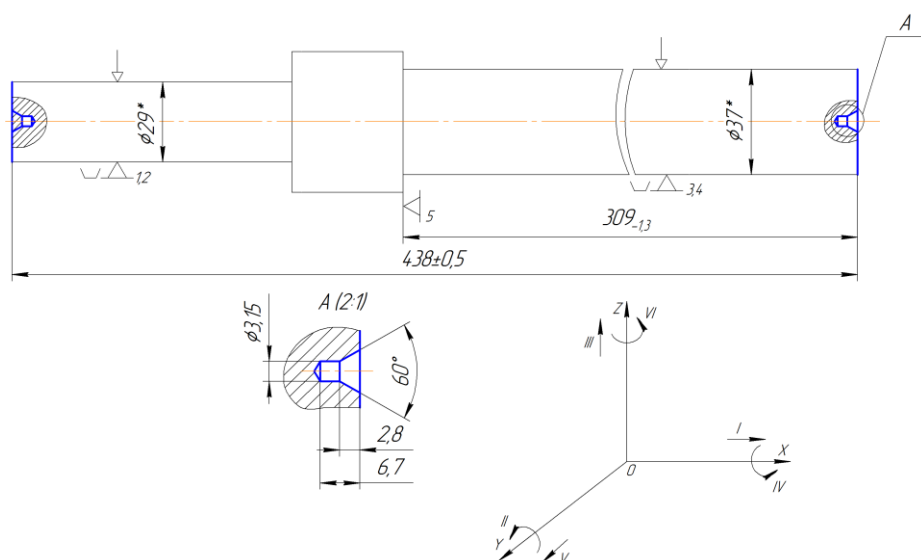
Схема базування деталі для фрезерно-центрувальної операції (варіант 1)
